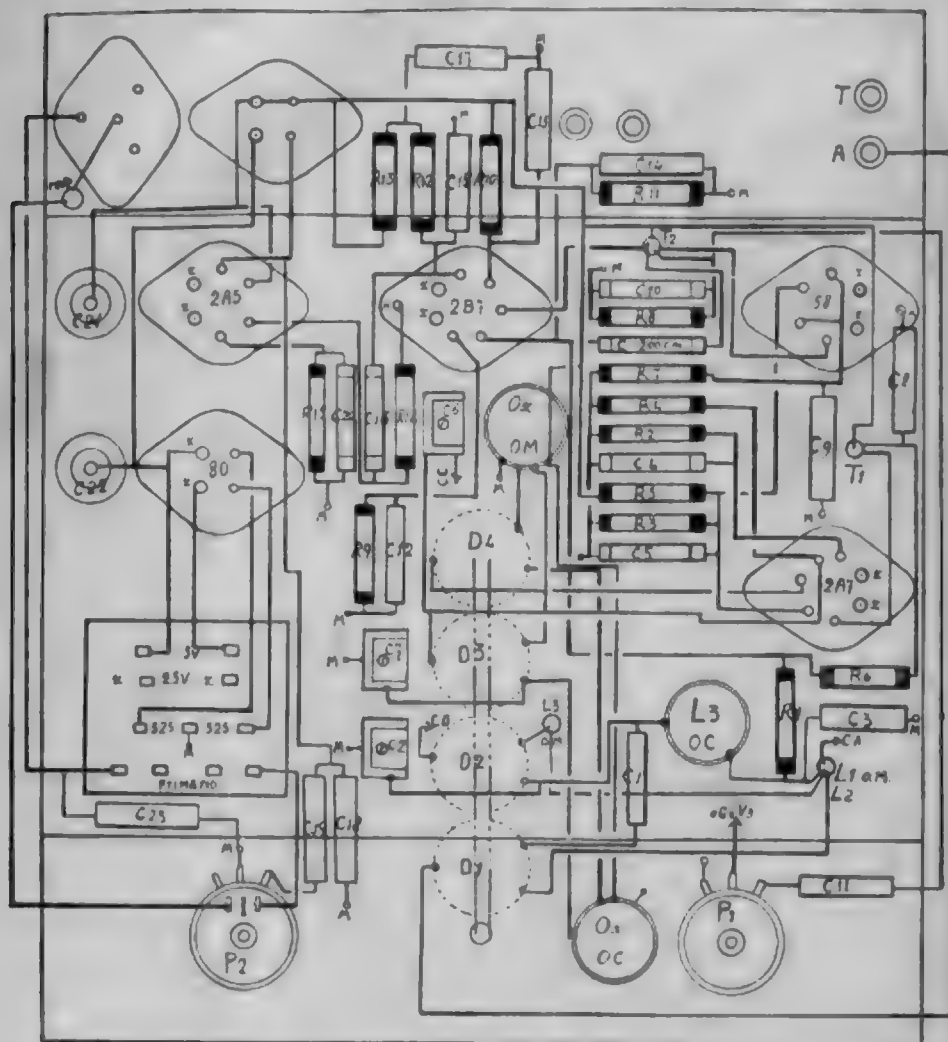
Piano di costruzione dell'apparecchio M 5.
